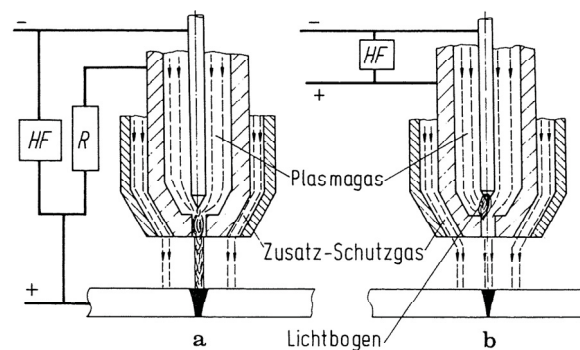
Plasmaschweißen: a Plasmalichtbogenschweißen; b Plasmastrahlschweißen [9]
